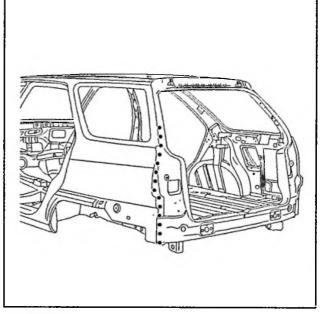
СР09НС Souder par points "bouchon" MAG. Meuler les points de soudure MAG.
